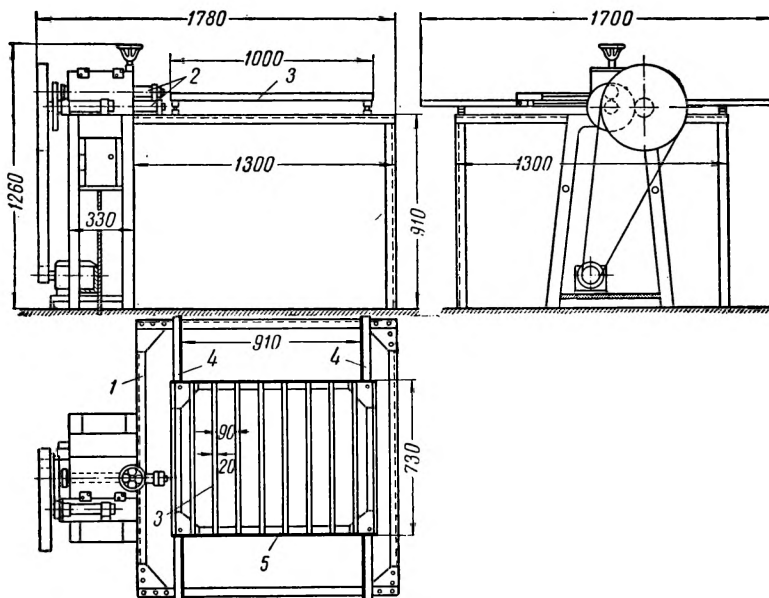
Станок конструкции И. П. Прохорова для обрезки нестандартных листов кровельной стали
